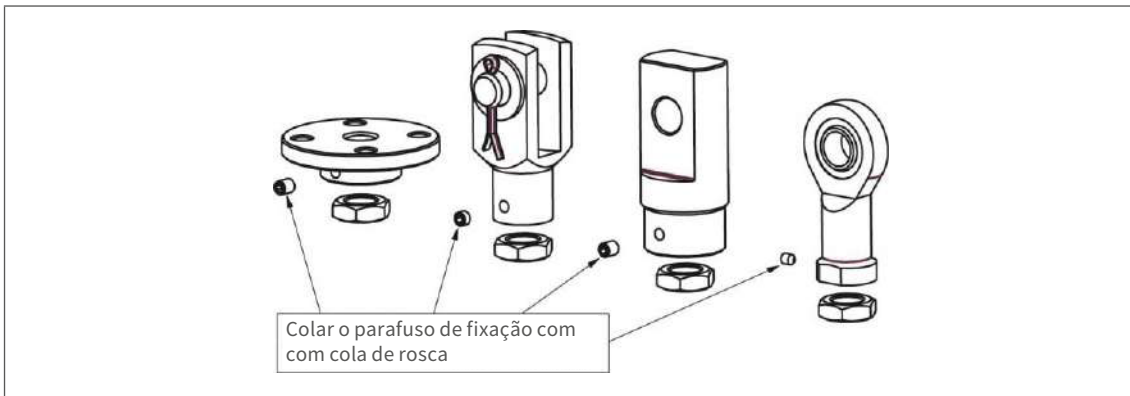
Fixar flanges, forquetas, apoios oscilantes, olhais após ajustar a posição.
